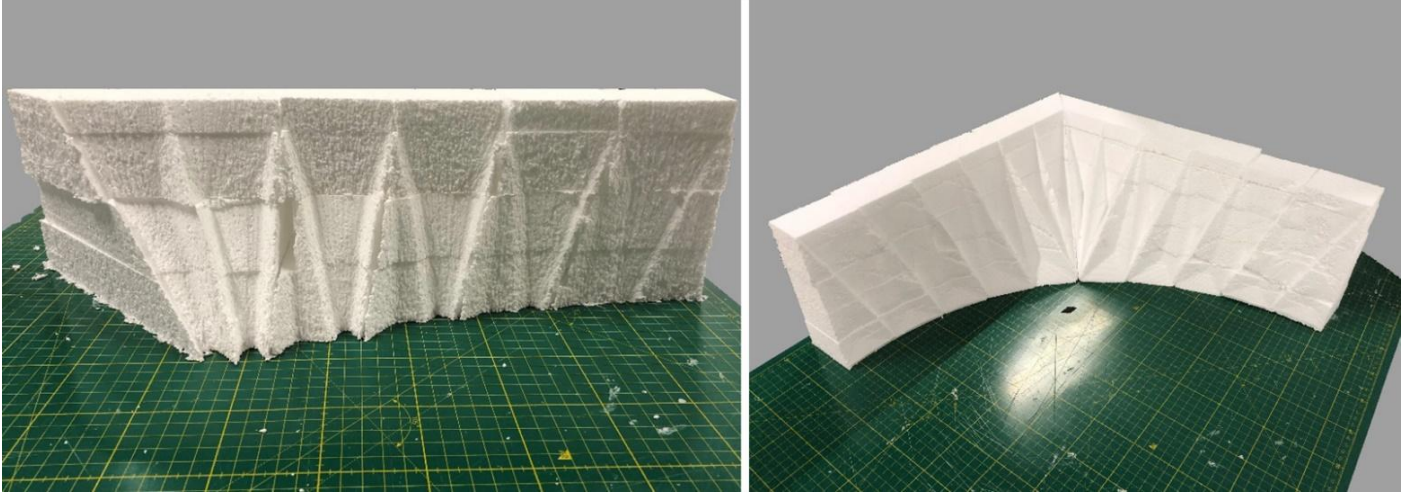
Robot kola entegre edilmiş spindle motor ile gerçekleştirilen frezeleme işlemleri
